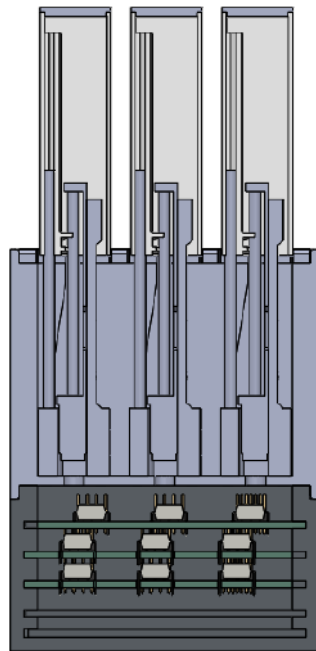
Vue en coupe du module sujet assemblé
